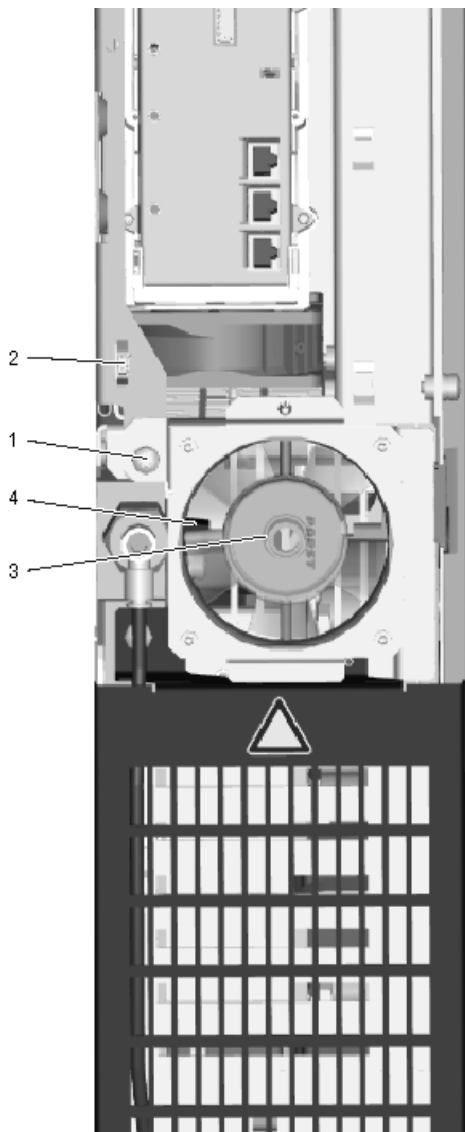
Демонтаж вентилятора электронного оборудования для использования вентиляционного рычага
